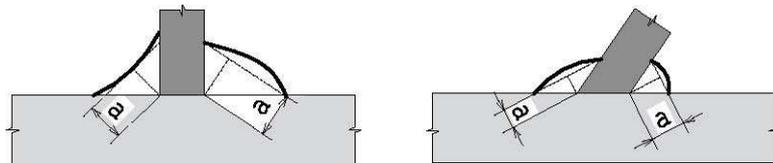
Definizione dell'area di gola per le saldature a cordone d'angolo
